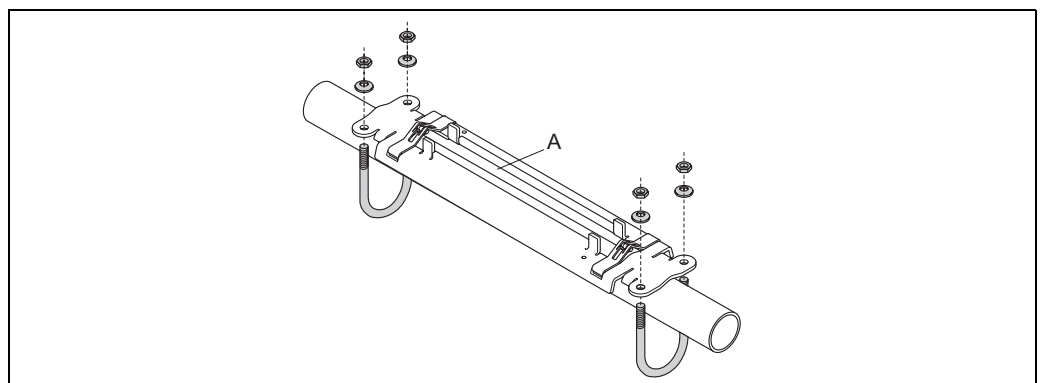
Montaggio con cavallotti a U del supporto per il sensore (DN 15...65 / ½...2½")
